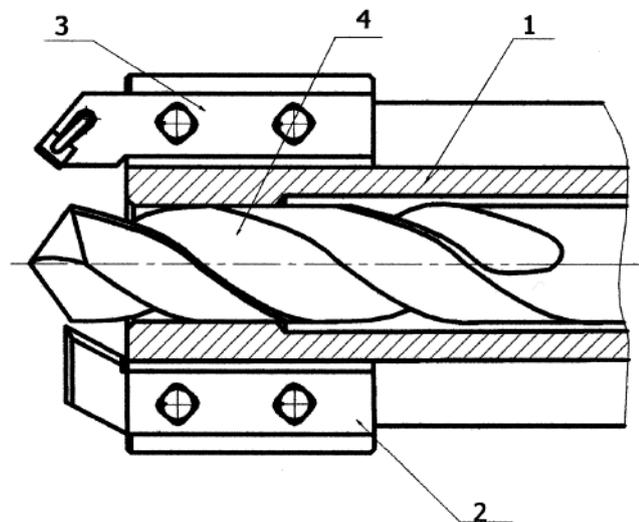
Инструментальная головка: 1 – корпус; 2, 3 – подрезной и проходной резцы; 4 – сверло.
